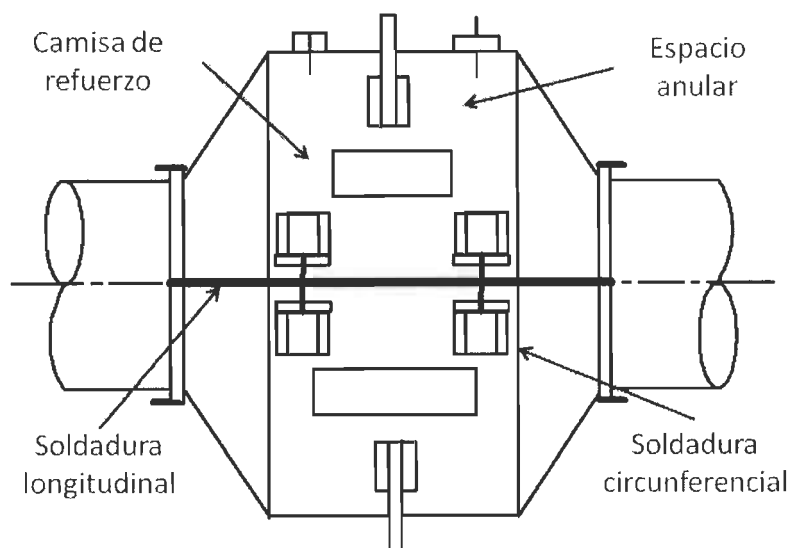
Encamisado Completo tipo B con soldadura circular y soldadura longitudinal con espacio anular, diseñado como contenedor de presión [16]
